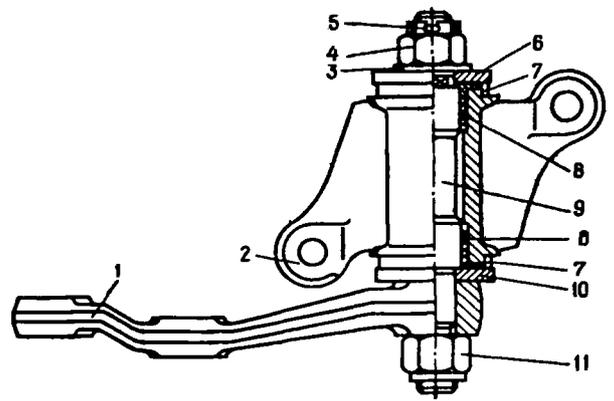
Разрез кронштейна маятникового рычага: 1 - маятниковый рычаг; 2 - корпус кронштейна; 3 - шайба; 4 - регулировочная гайка; 5 - шплинт; 6 - верхняя шайба; 7 - уплотнитель; 8 - втулка; 9 - ось рычага; 10 - нижняя шайба; 11 - самоконтрящаяся гайка
